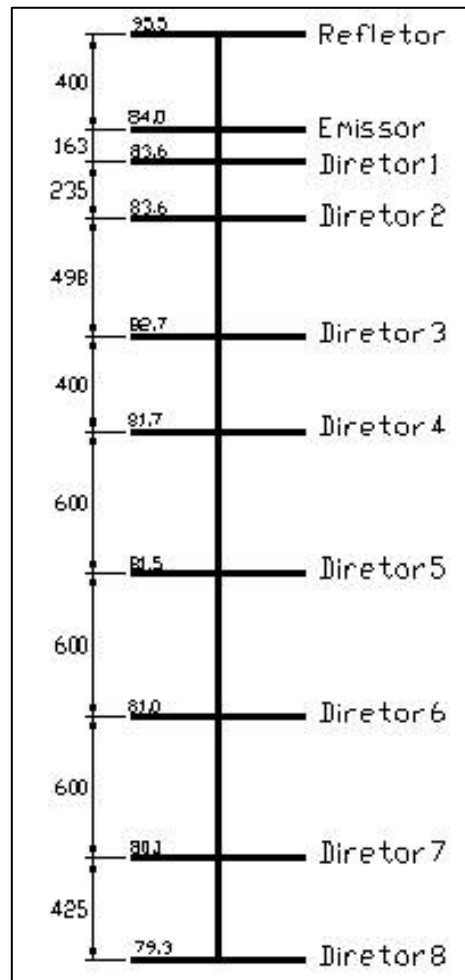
Planta estrutural de uma antena Yagi.
